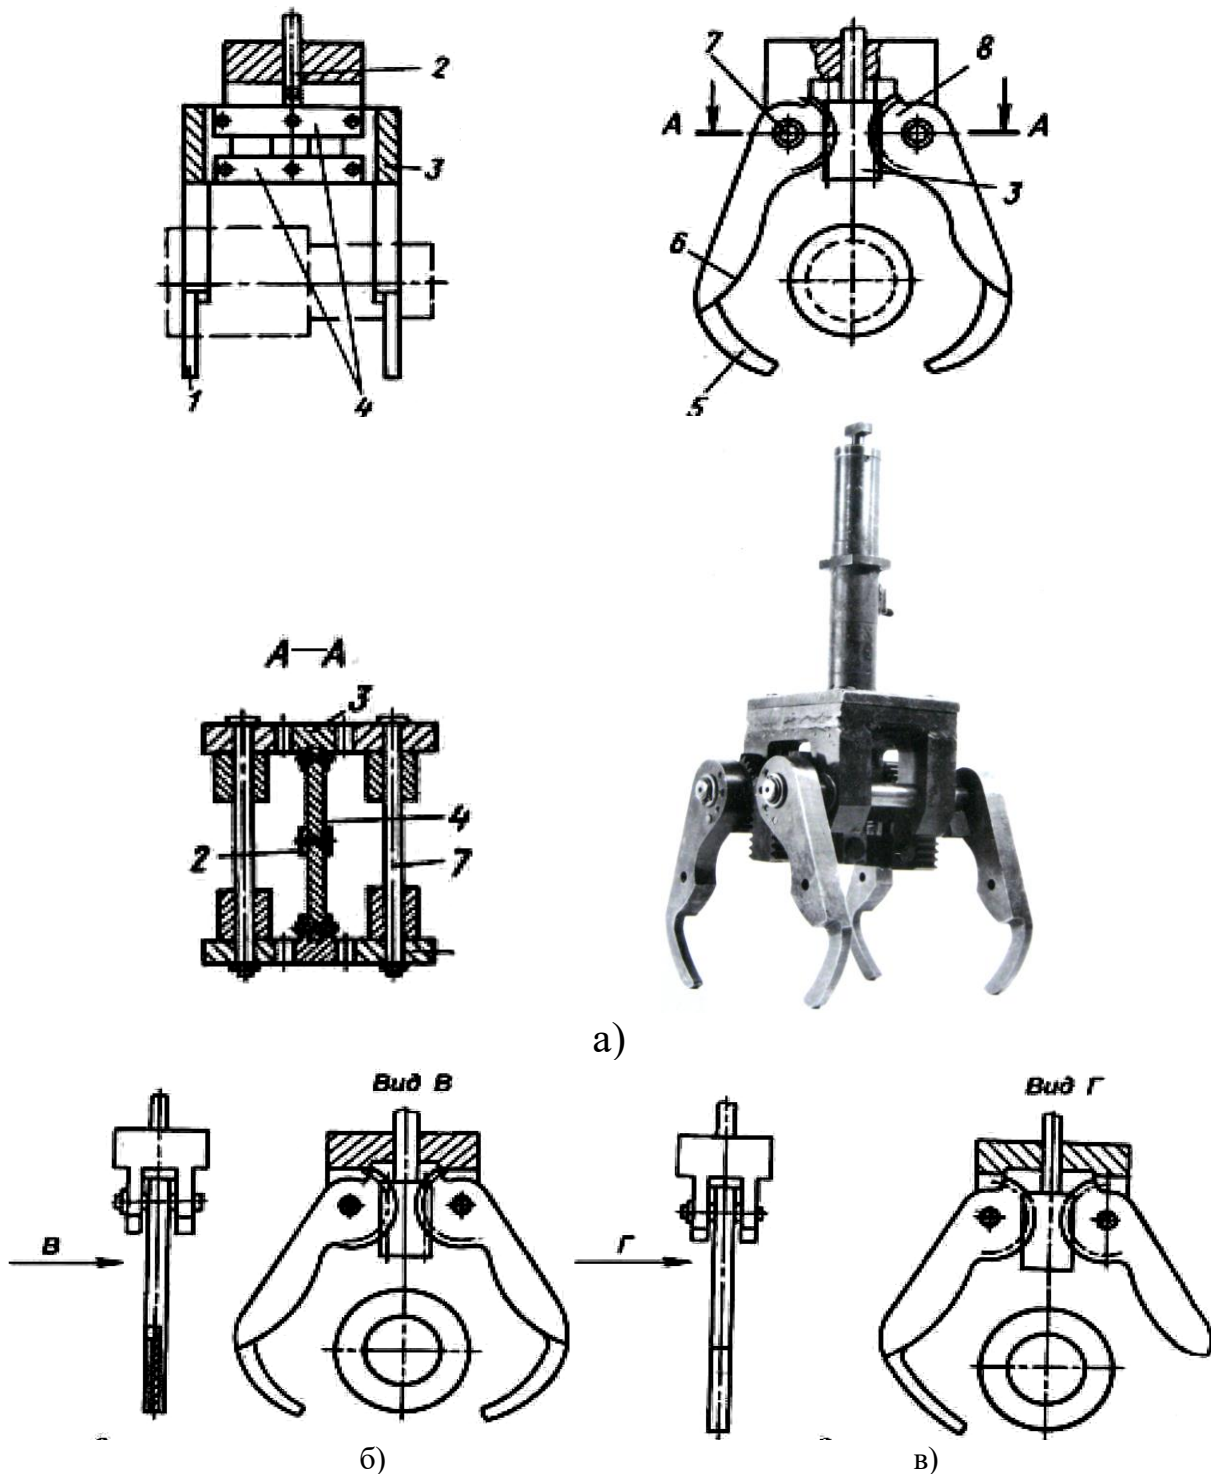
Широкодіапазонні ЗП з рейковими проміжними передачами:
